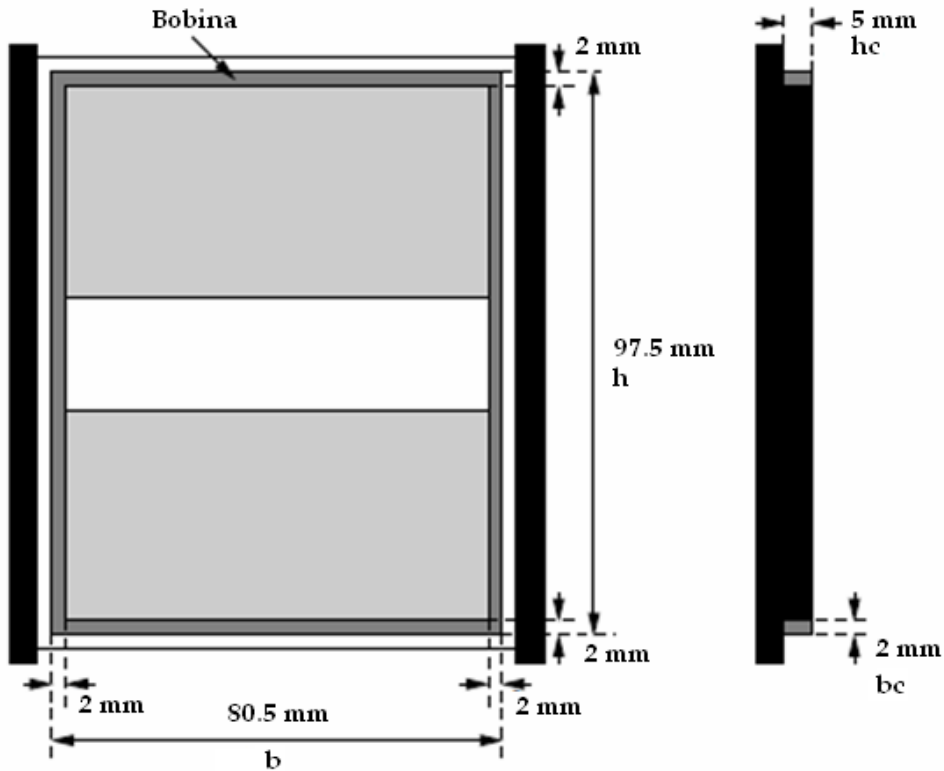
Dimensiones del magnemagnetopar de forma rectangular
